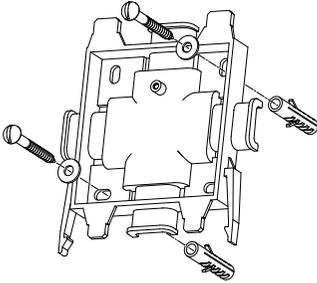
Visser le support mural/sur conduite avec les rondelles plates
